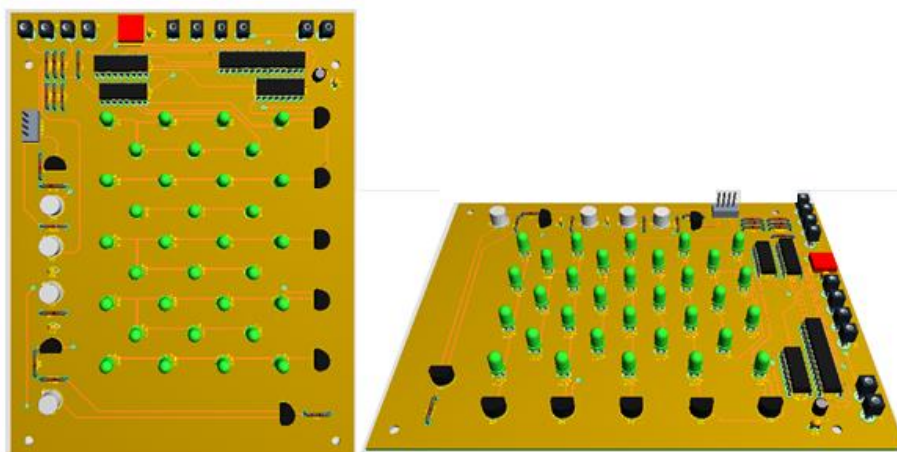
Vista en 3D de la PCB dissenyada.
